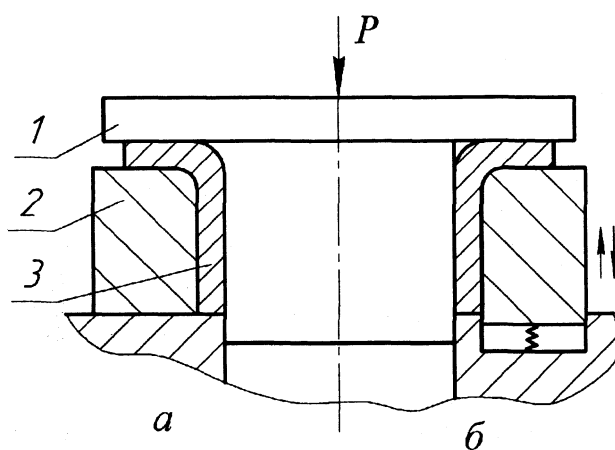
Схема раздачи (а) и осадки (б) трубной заготовки: 1 – пуансон; 2 – матрица; 3 – заготовка
